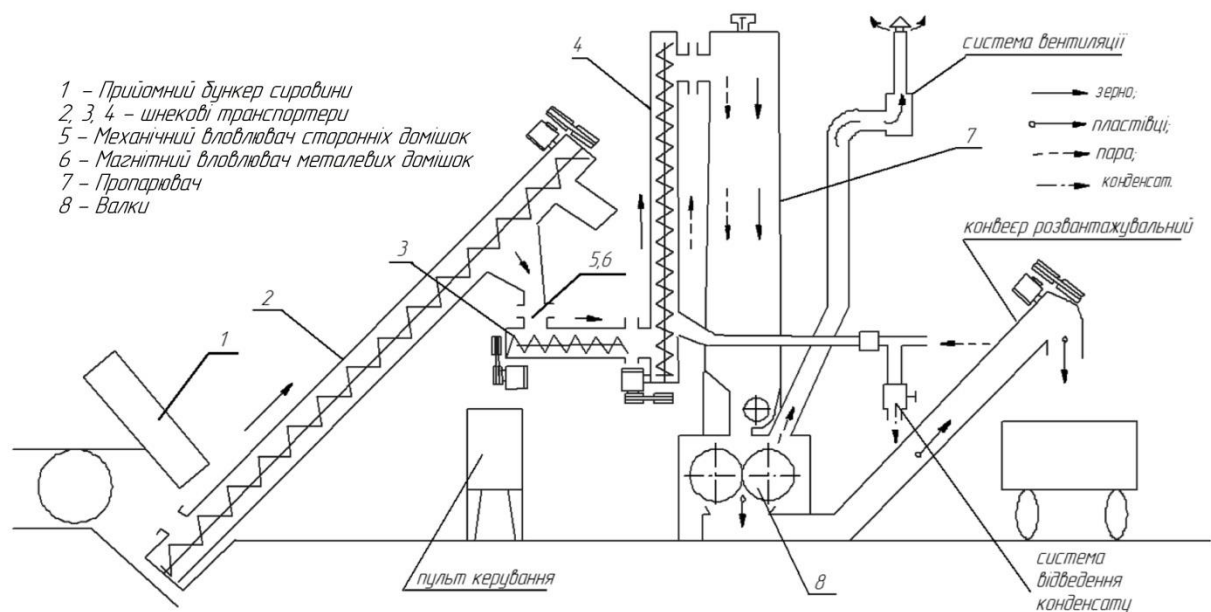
Конструкторсько-технологічна схема плющильного агрегату для обробки зерна.
